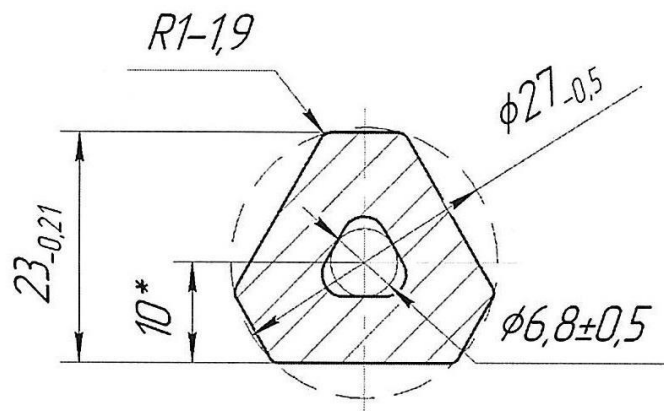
Поперечное сечение штанги ШБТ 23-L/23-M16
